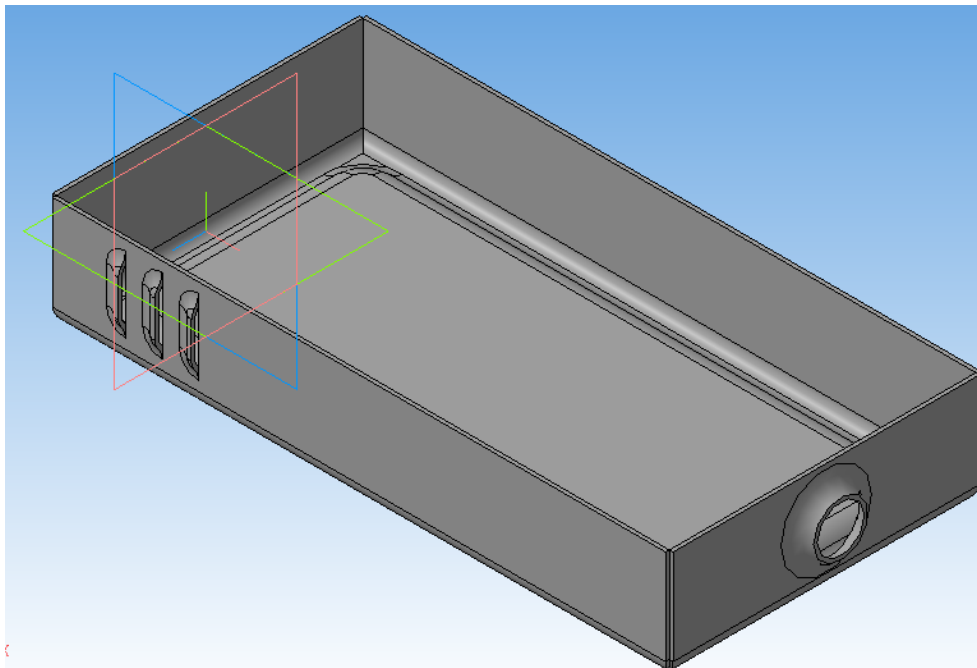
3D-модель листової деталі, створеної з використанням штампування
